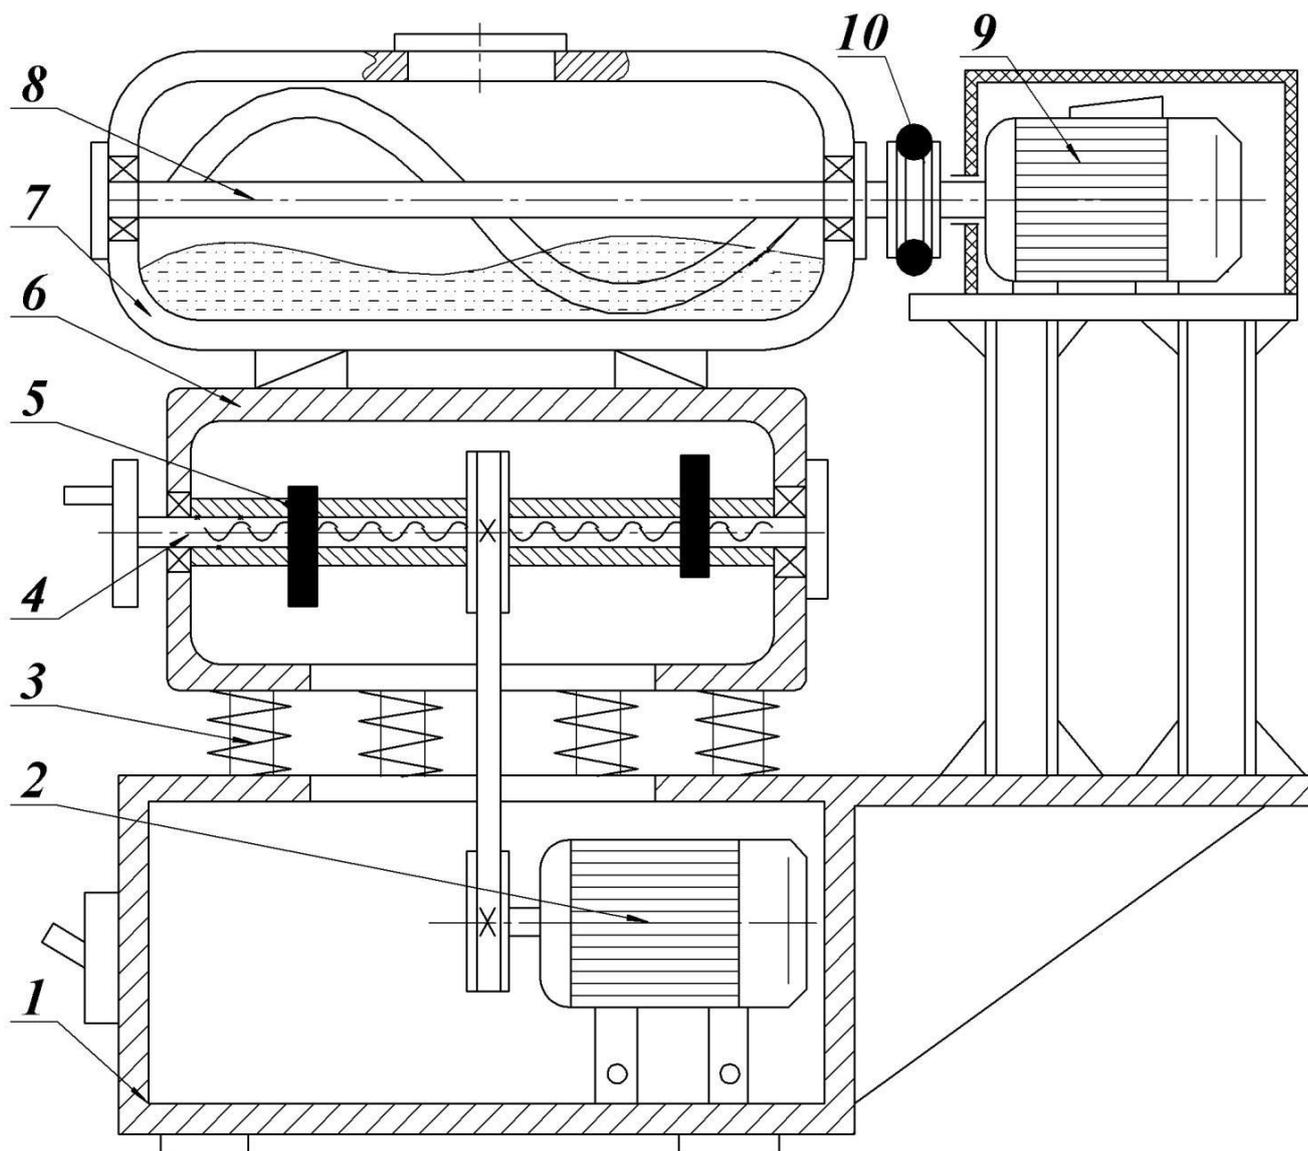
Принципова схема установки для віброабразивної обробки з горизонтальним положенням активного робочого органу
